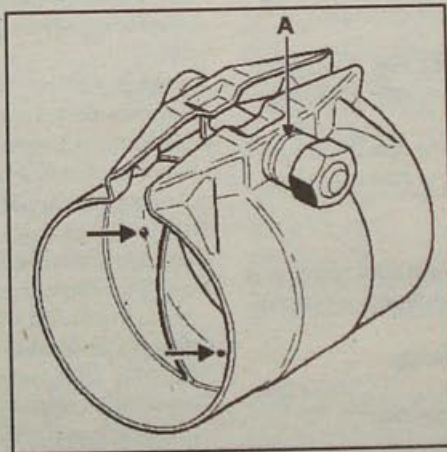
Ремонтный патрубок системы выпуска отработавших газов: А – канавка, определяющая момент затяжки гайки
